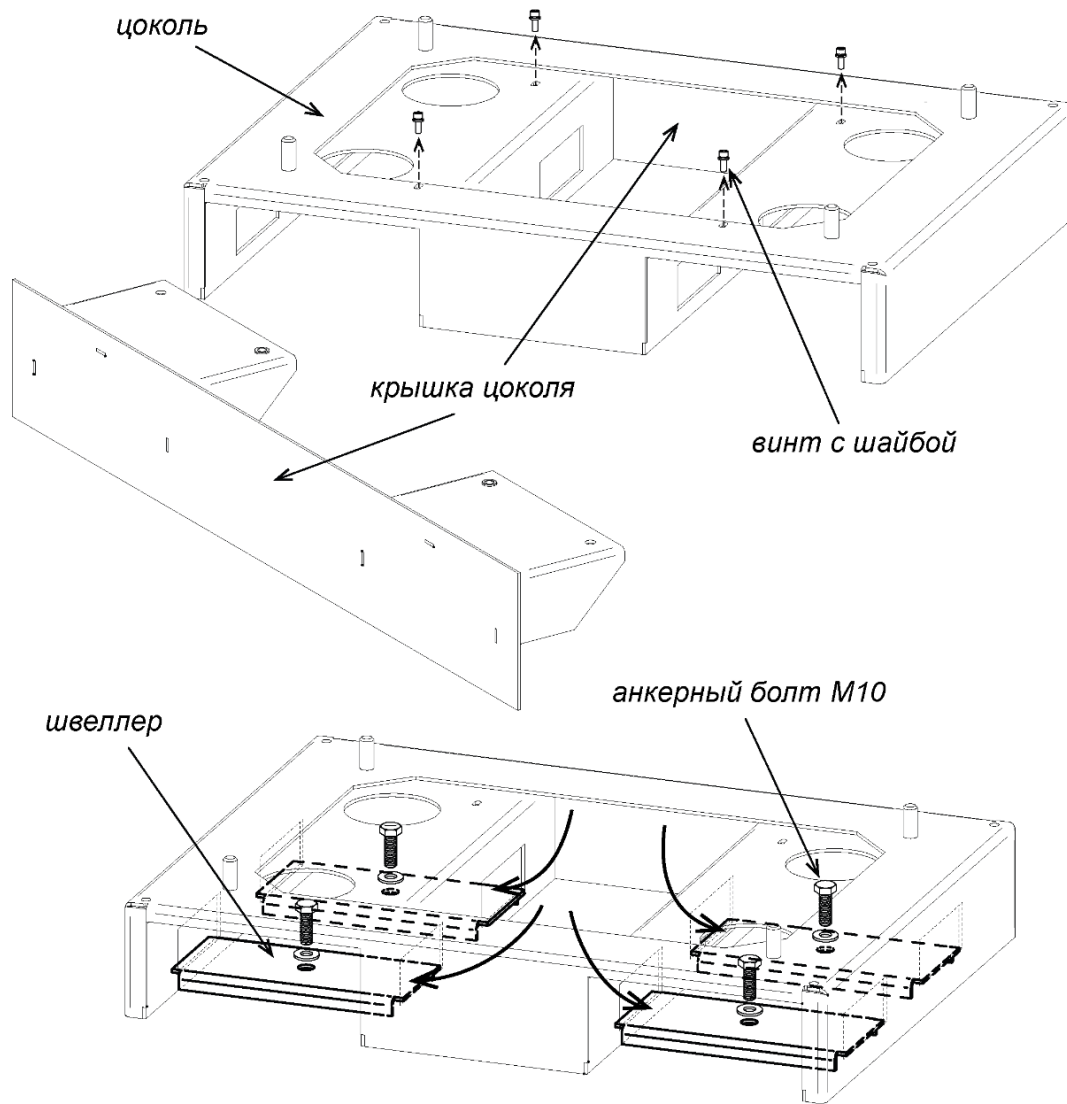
Конструкция цоколя и установка швеллеров для крепления паркомата на установочной поверхности
